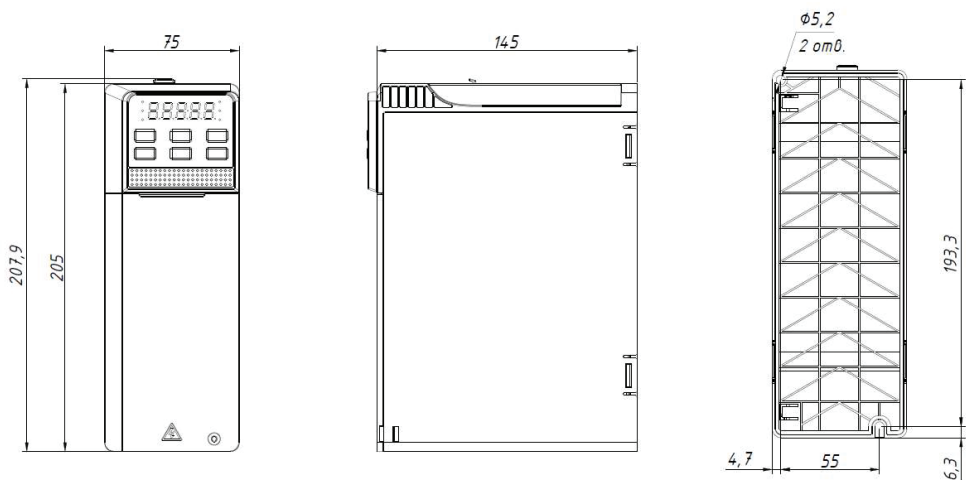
Чертеж преобразователя частоты типоразмера С2
